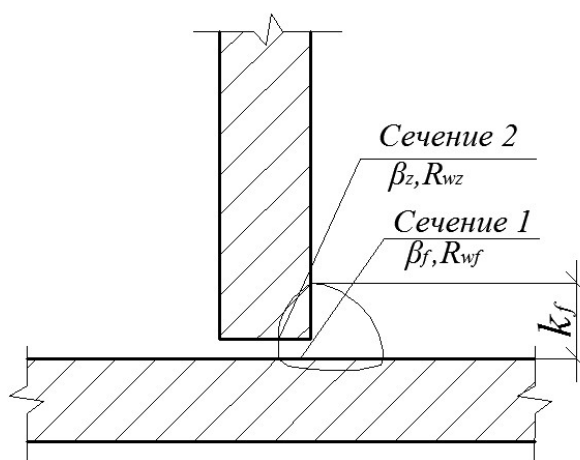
Схема расчетных сечений сварного соединения с угловым швом
